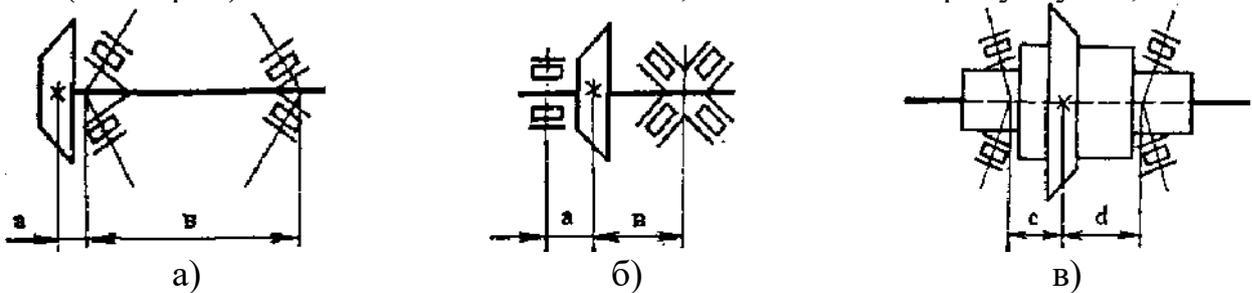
Схеми встановлення зубчастих коліс і підшипників головної передачі
